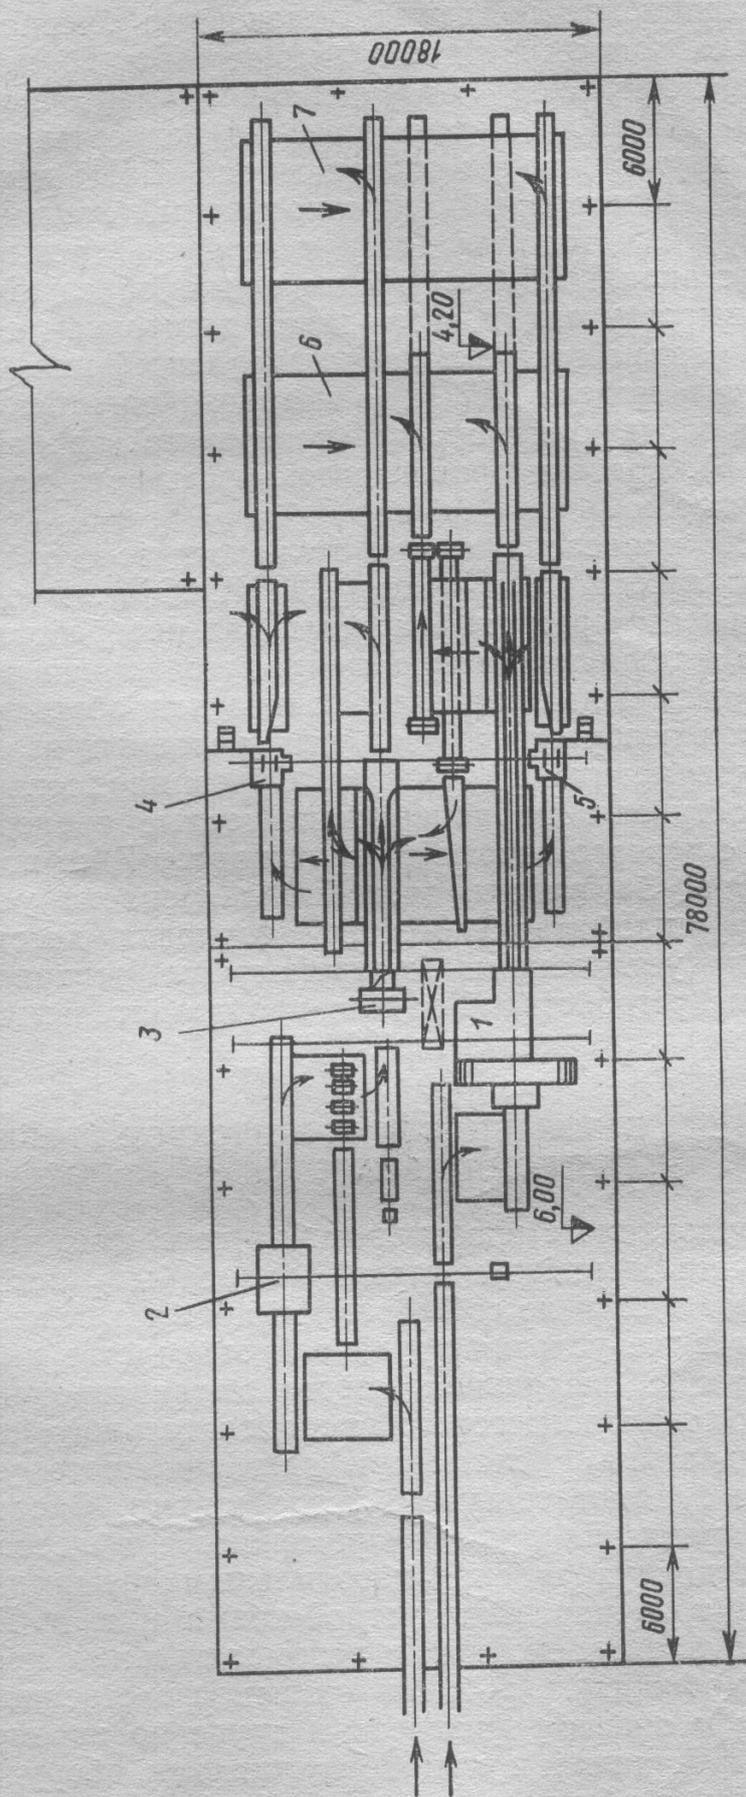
Схема технологического процесса в двухпуточном лесопильном цехе с фрезерными агрегатами и фрезерными агрегатами:
